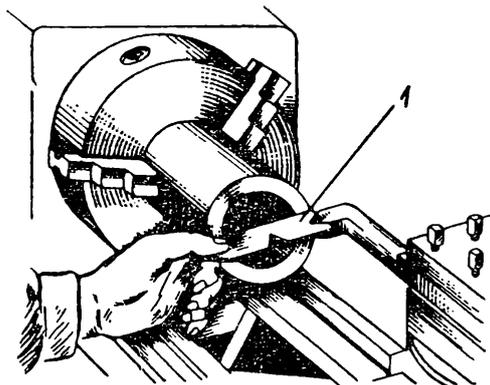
Установка резца по шаблону для нарезания внутренней резьбы (1 — шаблон)
